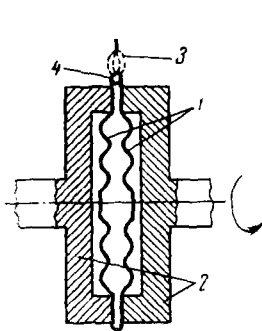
Схема арго-но-дуговой сварки мембраны:
